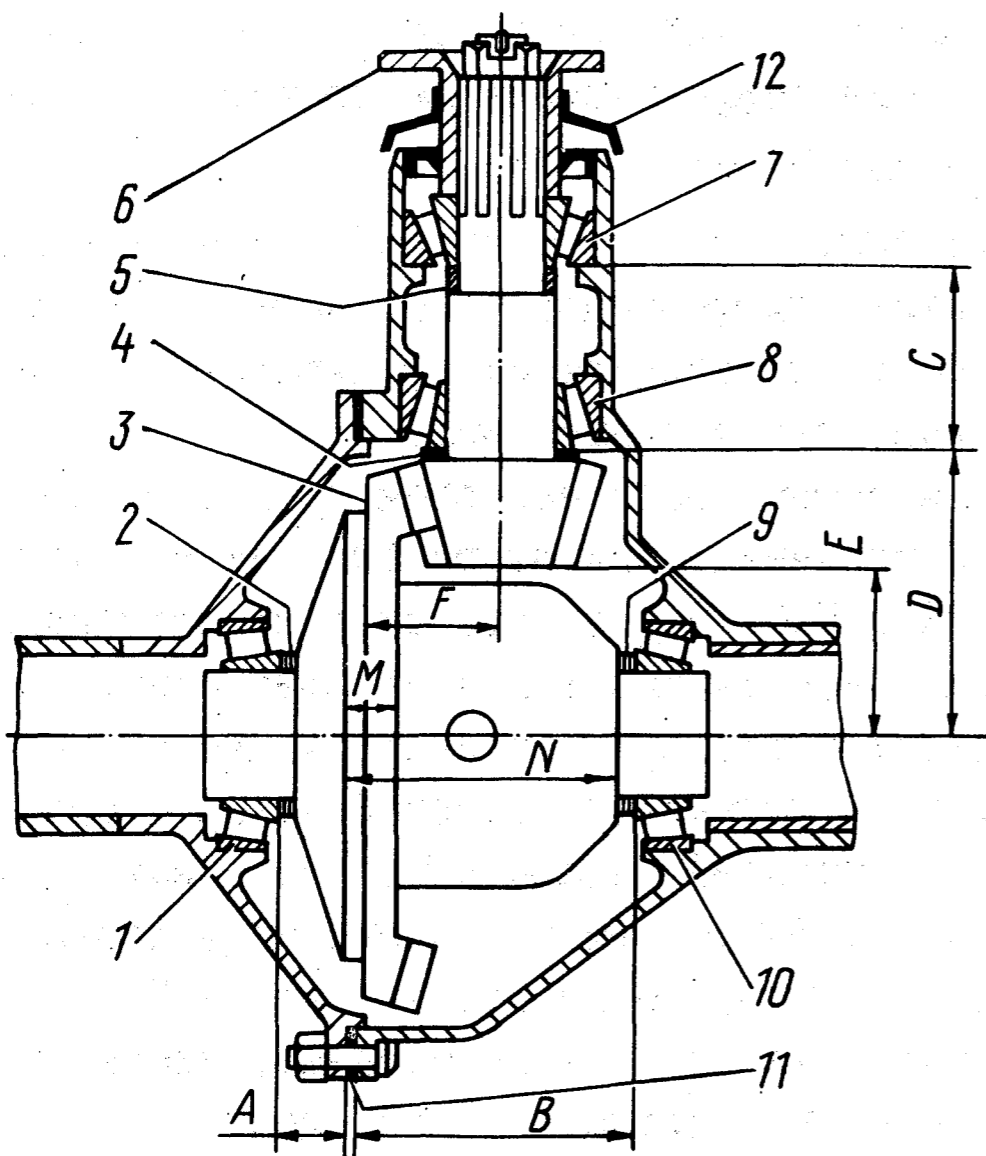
Схема регулировки главной передачи: I и IO - подшипники дифференциала; 2 и 9 - прокладки подшипников дифференциала регулировочные; 3 - шестерня ведомая; 4 - кольцо установки ведущей шестерни регулировочное; 5 - шайба преднатяга подшипников регулировочная; 6 - фланец; 7 и 8 - подшипники ведущей шестерни; II - прокладки (две) уплотнительные; 12 - грязеотражатель
